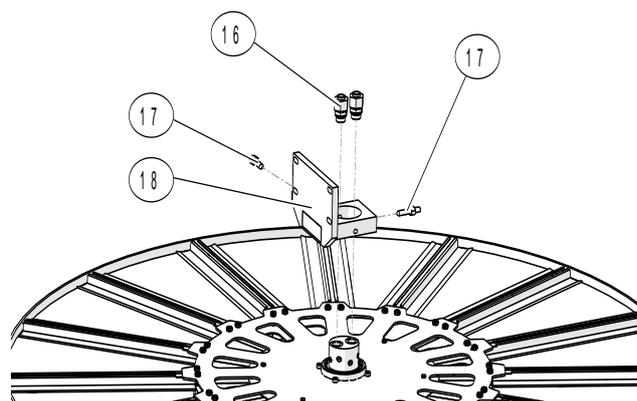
Hydraulik-Verschraubungen und Gewindestifte demontieren
